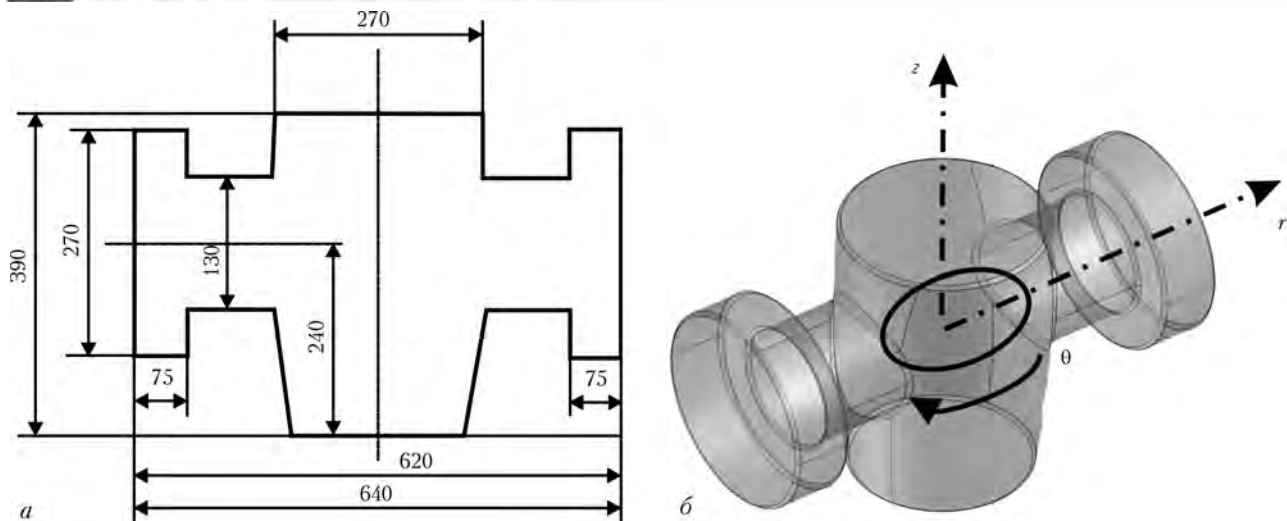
Заготовка корпуса фланцевой задвижки с условным проходом 80 мм: а — эскиз; б — изометрия
